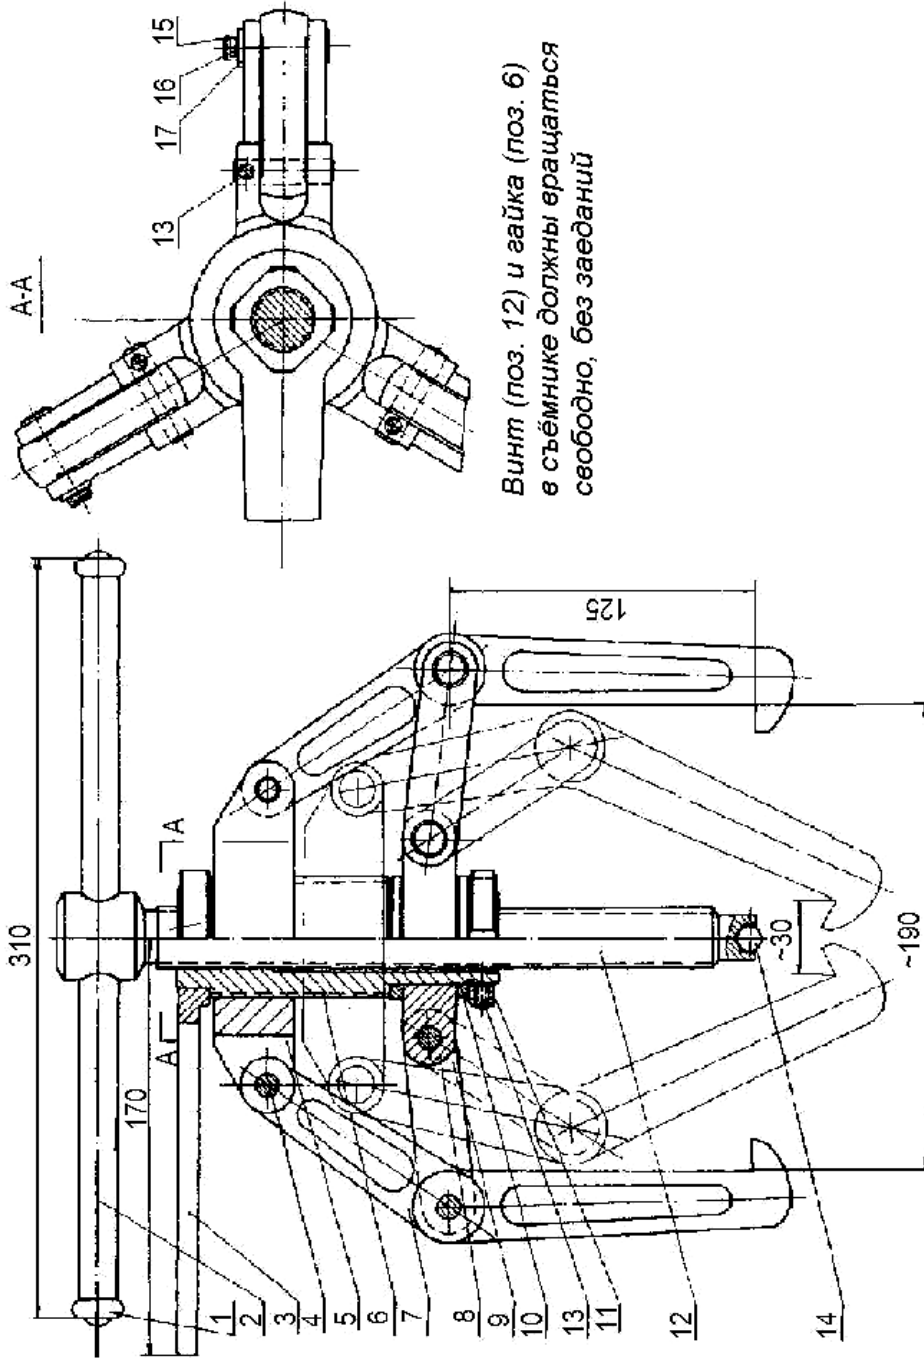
Универсальное приспособление для съёма деталей диаметрами от 30 до 190 мм:
